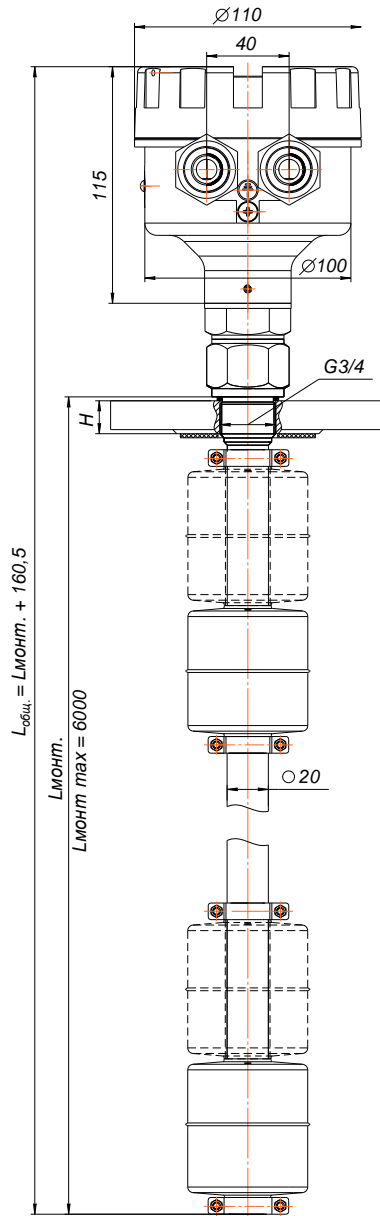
Габаритные и присоединительные размеры
